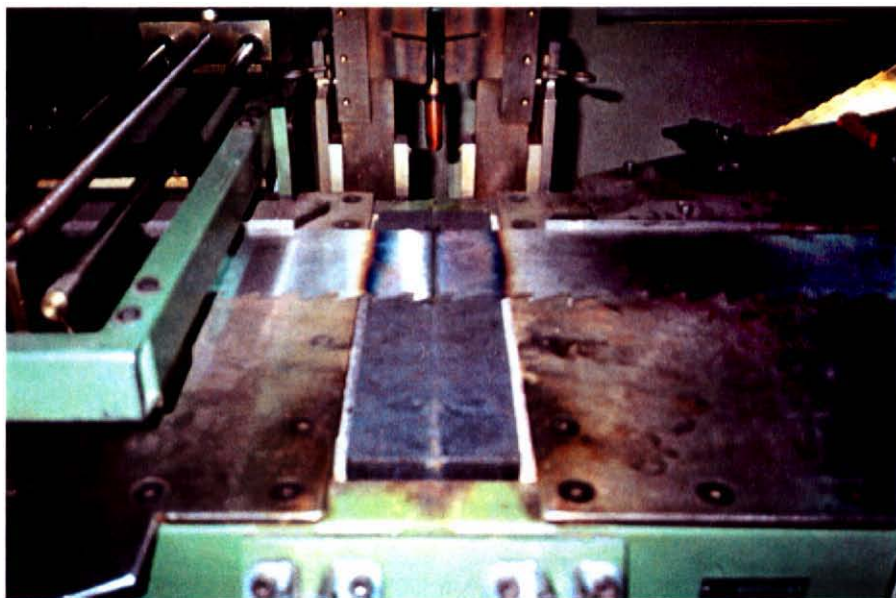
SOLDADURA TERMINADA, OBSÉRVESE LOS PEQUEÑOS TROZOS DE SIERRA COLOCADOS PREVIAMENTE EN LOS EXTREMOS DE LA JUNTURA.
